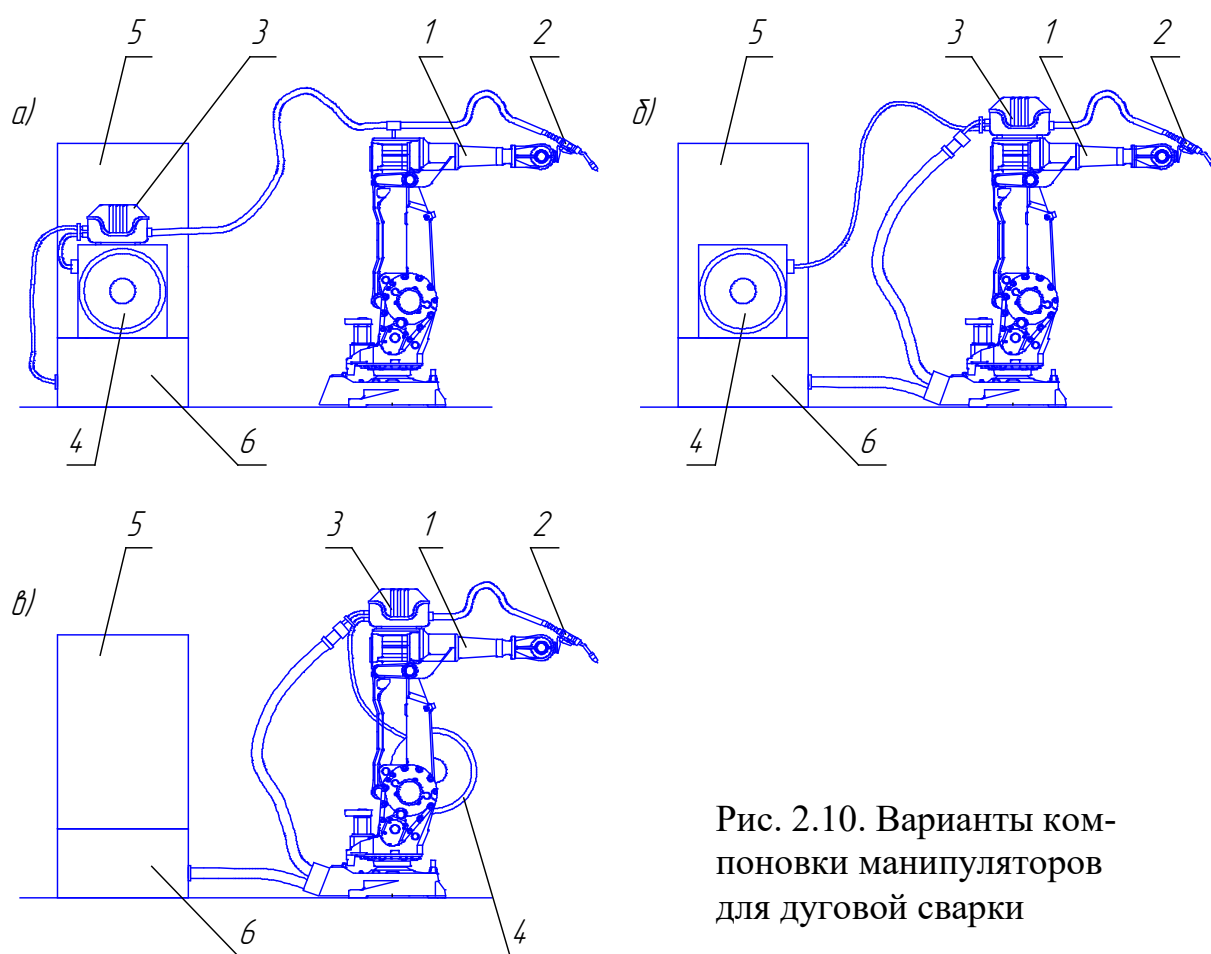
Варианты компоновки манипуляторов для дуговой сварки
